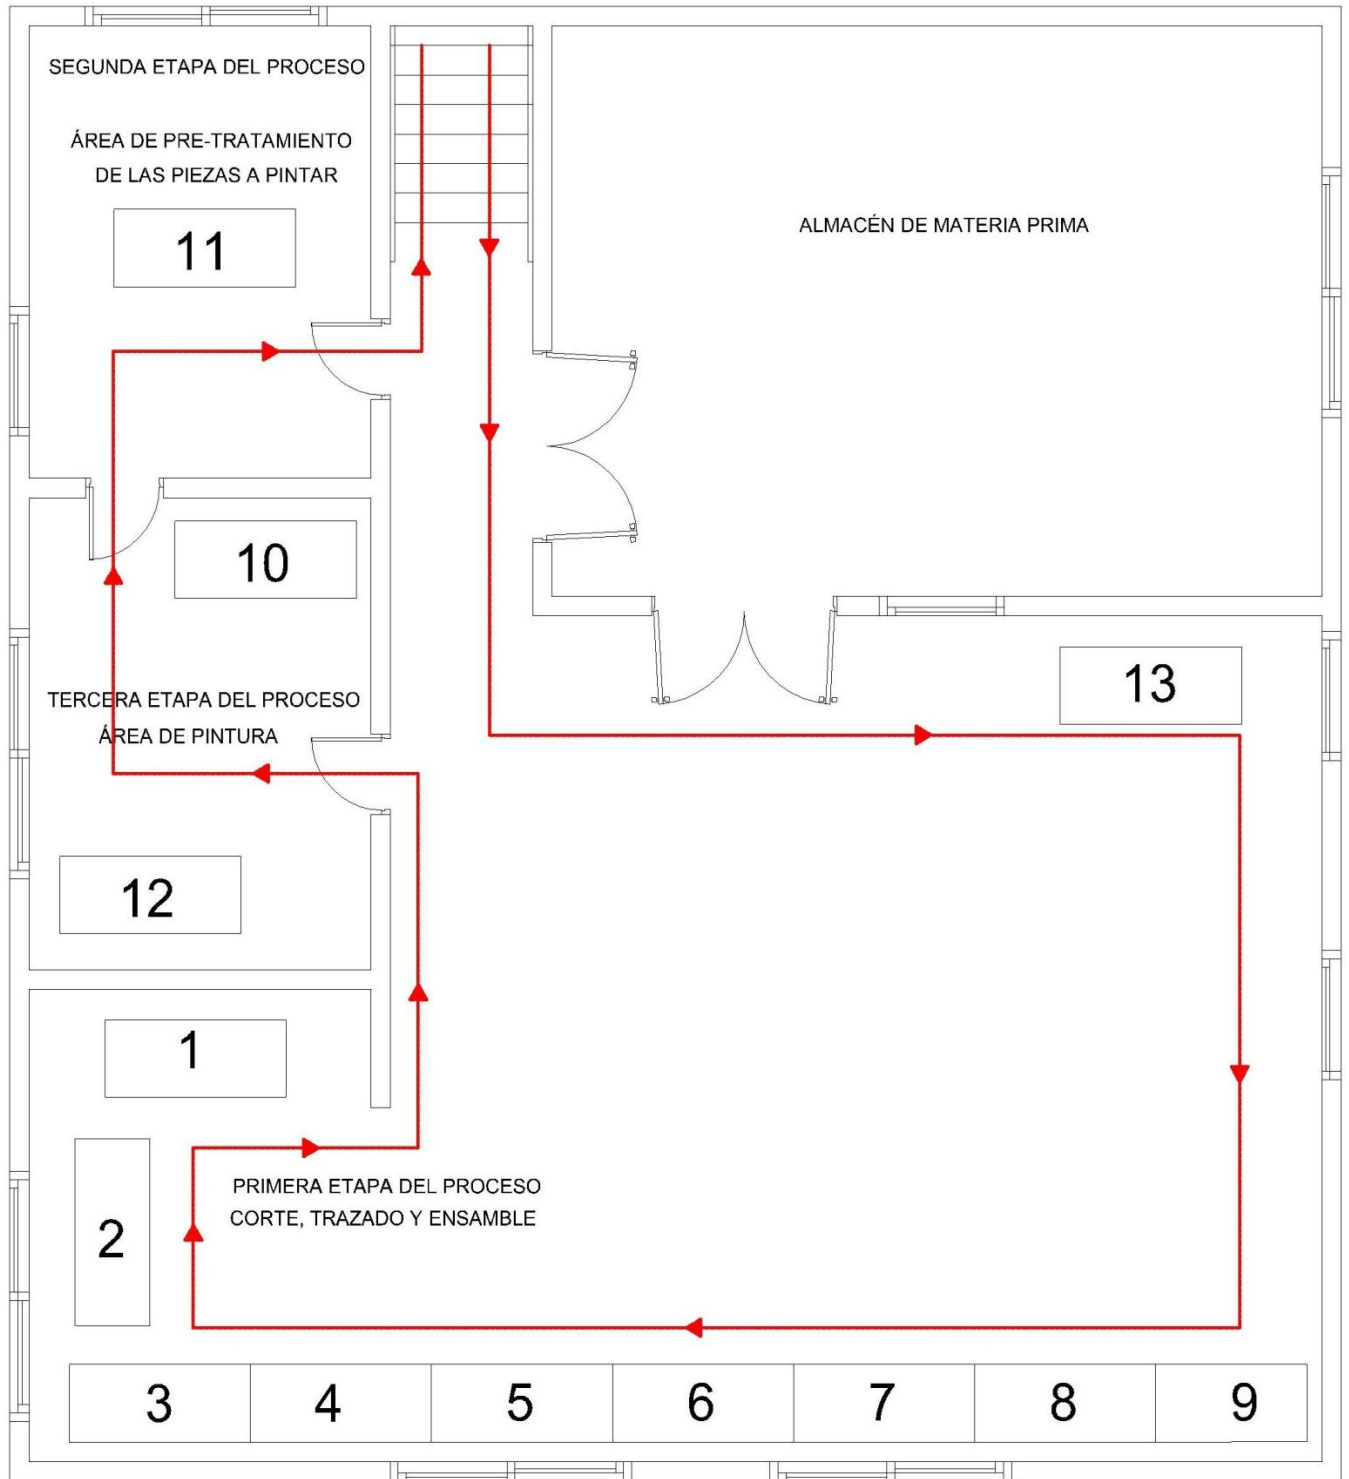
Plano: Recorrido en planta alta del Auditor de calidad. Fuente: Rondón (2018)
